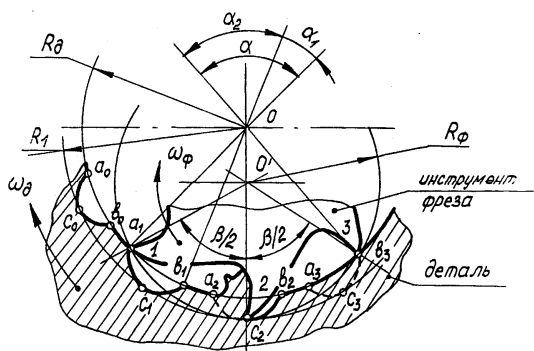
Схема обработки внутренней цилиндрической поверхности гильзы.
